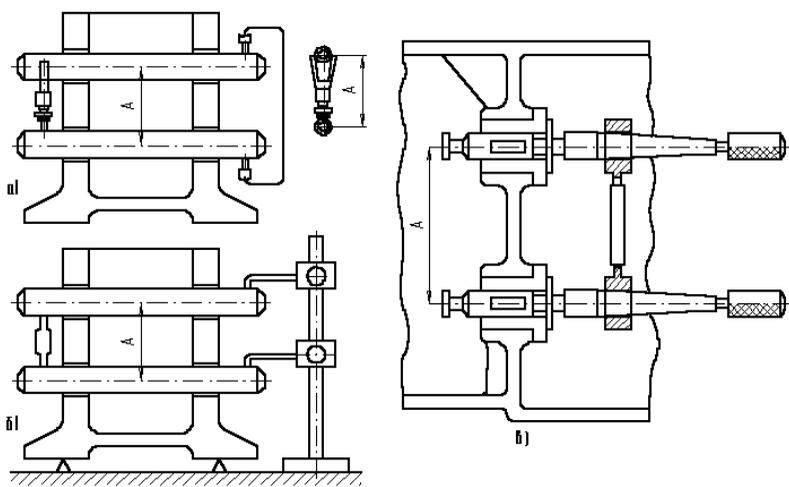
Схемы проверки расстояния между осями отверстий корпусов зубчатых передач:
